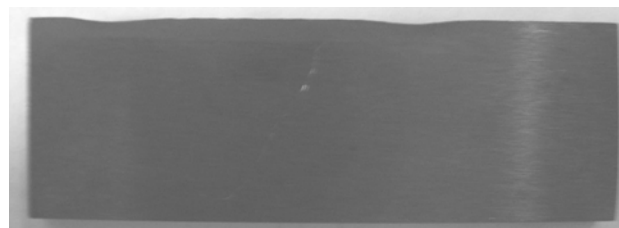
Фото резца, обрабатывающего кромки ДСтП
